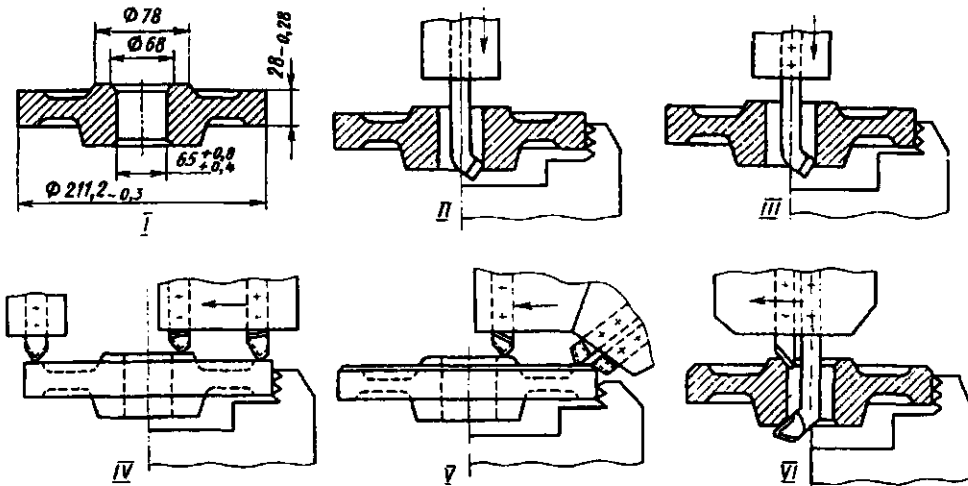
Наладка шестишпиндельного полуавтомата для обработки заготовок зубчатых колес в патроне
